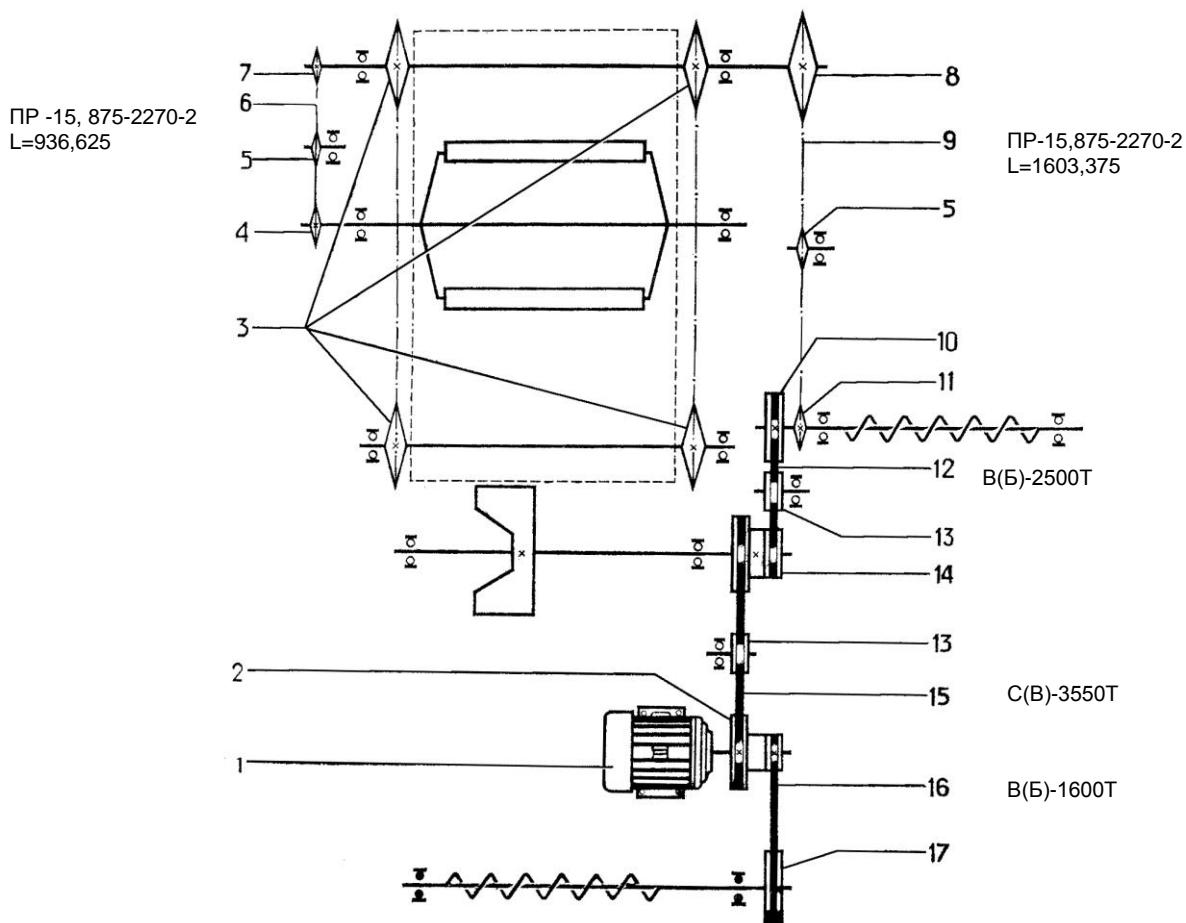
МПО 50.00.000. Схема расположения подшипников
